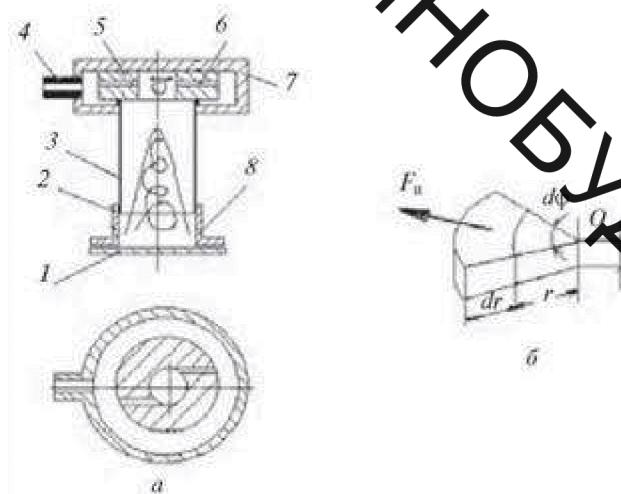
Пневмовихровий захоплювальний пристрій (*a*) і схема до розрахунку підйомної сили ЗП (*б*): 1 – ОМ; 2 – насадка, 3 – втулка, 4 – штуцер; 5 – завихрювач; 6 – сопла; 7 – корпус; 8 – вихідні отвори
